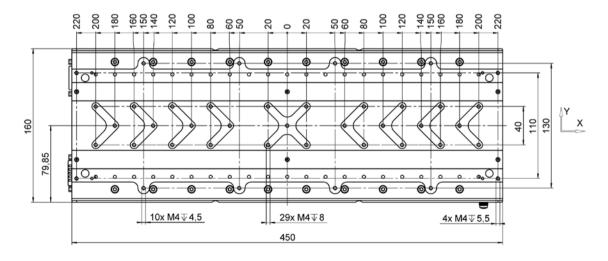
Abmessungen des V-551.7D: Draufsicht
